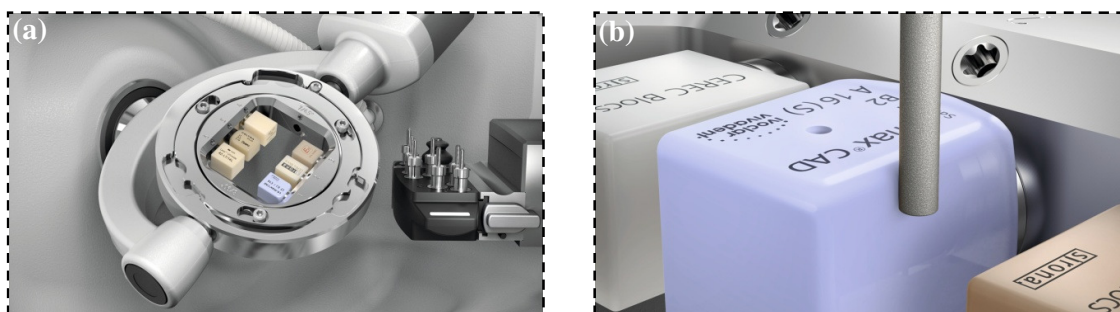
(a) Central de usinagem inLab MC X5<sup>®</sup>, da Sirona<sup>™</sup> utilizada nos ensaios de usinagem. (b) Conjunto de ferramentas utilizado no processo de usinagem.
